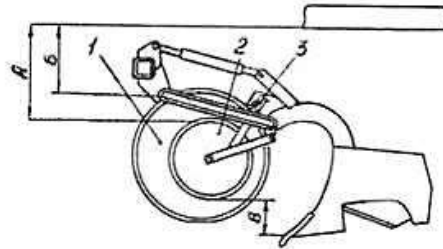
Схема регулювання глибини сошника: 1 – колесо; 2 – копіювальне колесо; 3 - важіль копіюючого колеса
